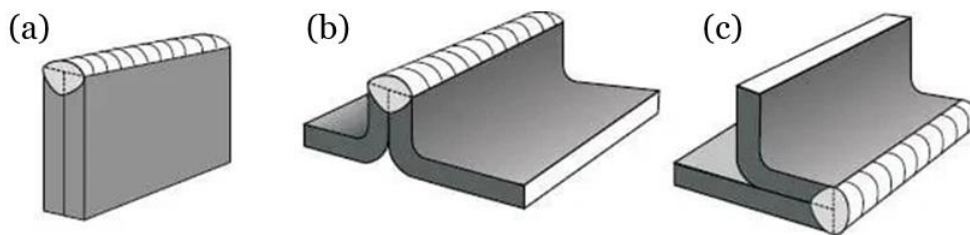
Resultado final de la unión de dos sustratos realizado mediante soldadura: (a) soldadura junta de borde en unión de borde, (b) soldadura junta de borde en una unión a tope con brida y (c) soldadura junta de borde en una unión en esquina con brida (Tipos de Uniones Soldadas: Guía Completa Sobre Soldaduras y Usos, n.d.).
